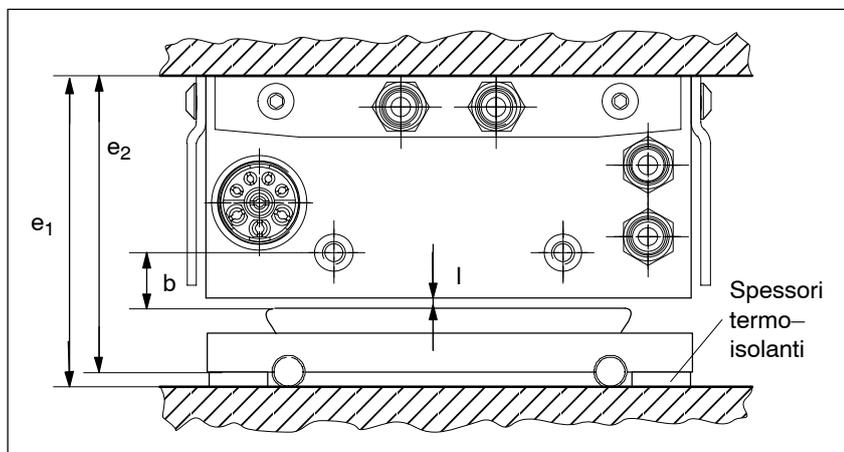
Dimensioni di controllo per il montaggio del motore 1FN1
